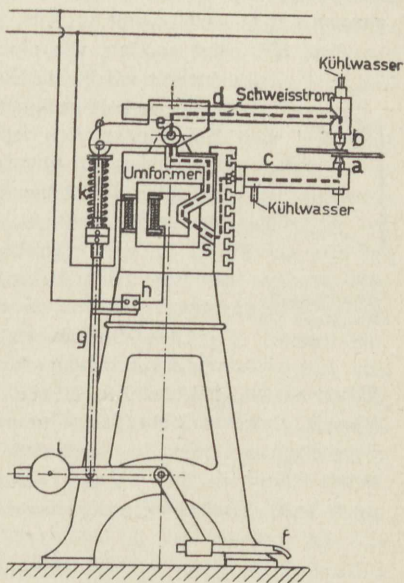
Schema einer elektrischen Punktschweißmaschine.
